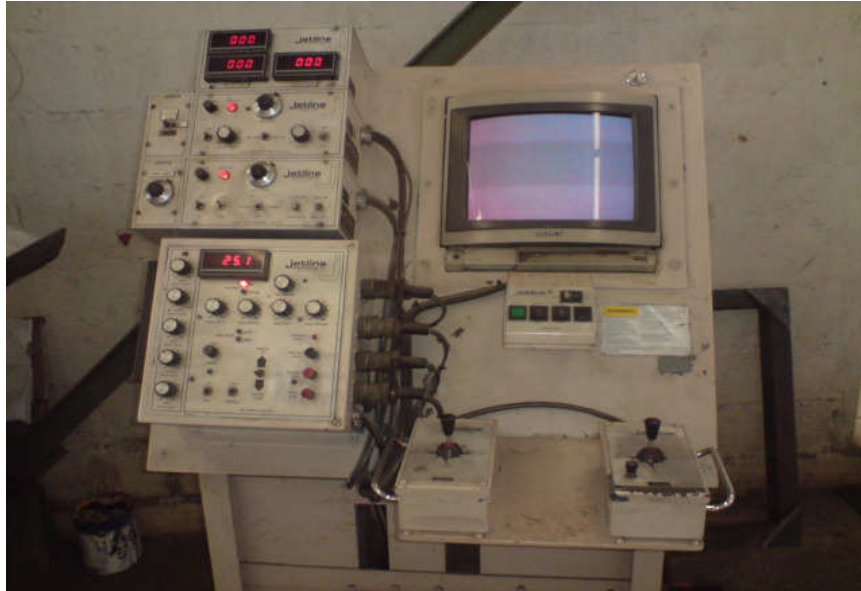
Máquina de soldagem: Jetline Engineering S/A 85425.
